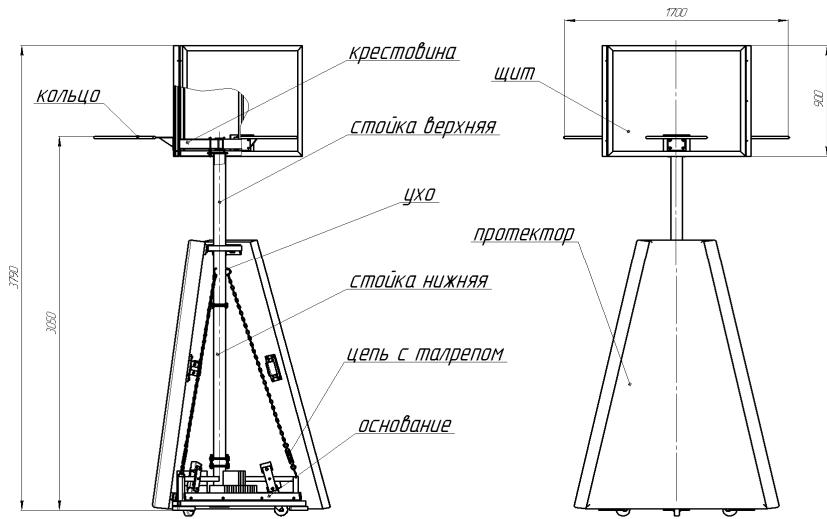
Схема конструкции стойки, ее монтаж и габаритные размеры.
